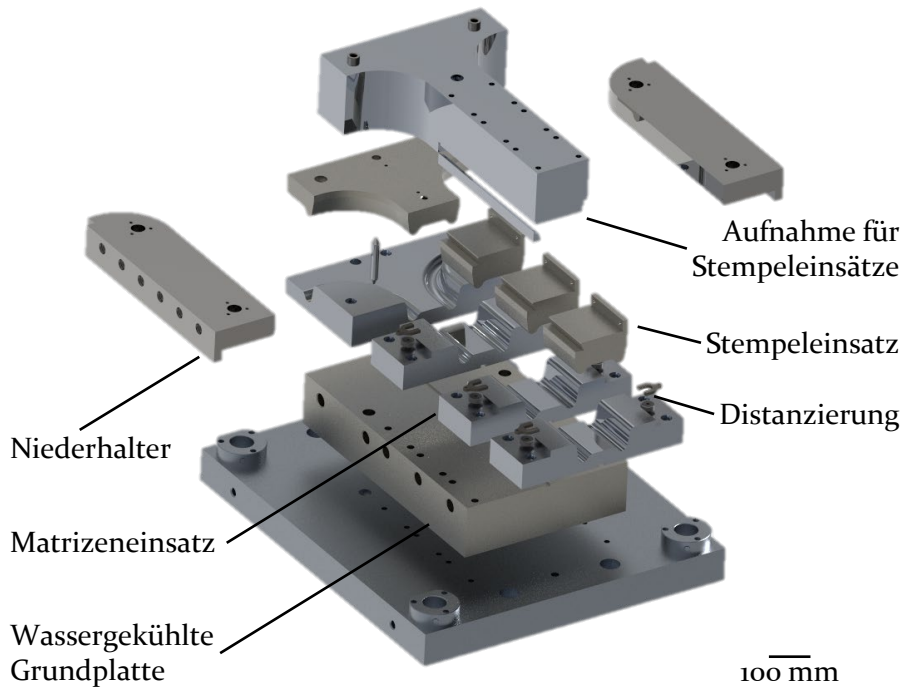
Aufbau des Demonstratorwerkzeugs (CAD-Modell)
